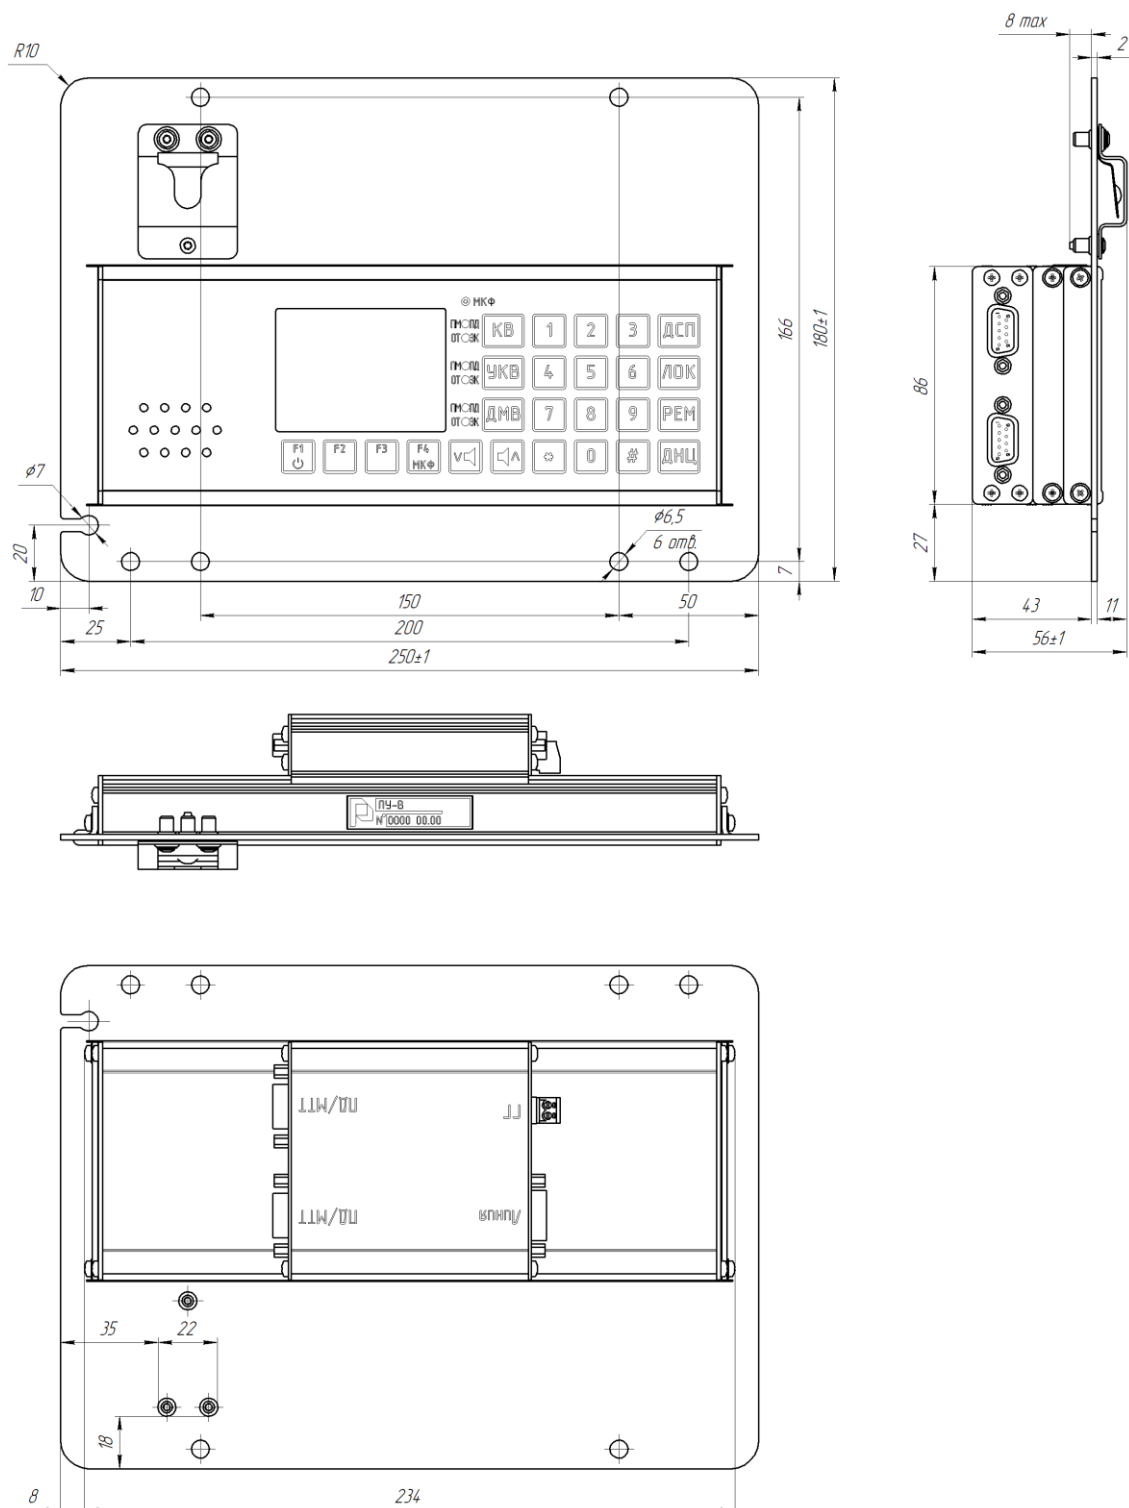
Габаритные и установочные размеры ПУ-В
